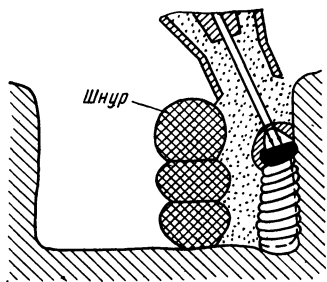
Наплавка отвесной стенки ящичного калибра при горизонтальном положении оси вращения вала
